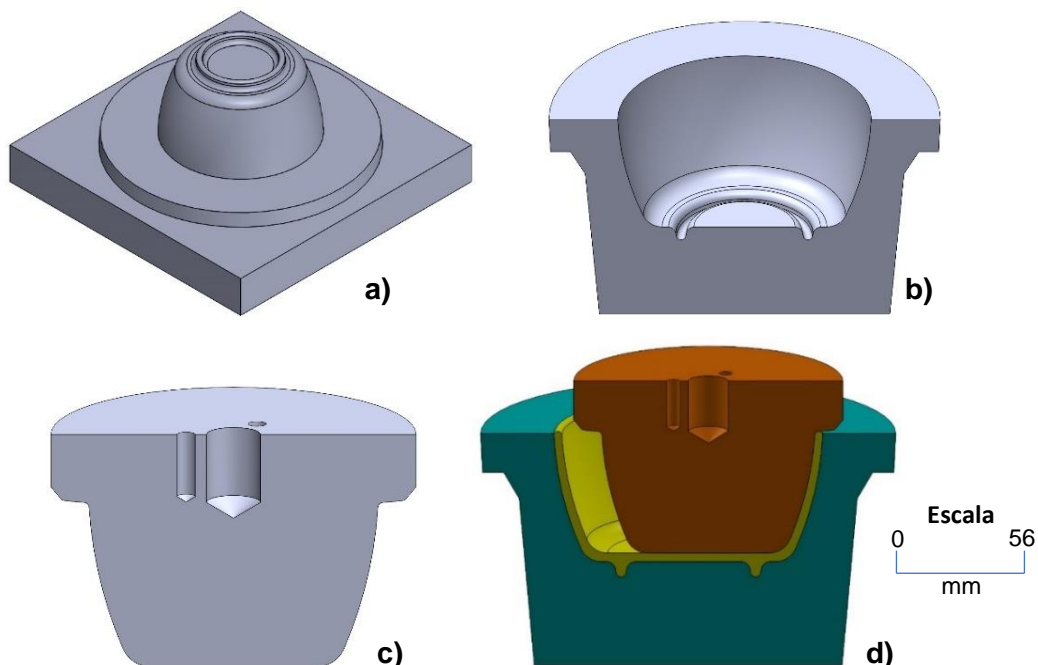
Componentes necessários para a conformação Roller da tigela do projeto: a) madre; b) molde; c) calibrador e d) conjunto do molde, da tigela e do calibrador.
